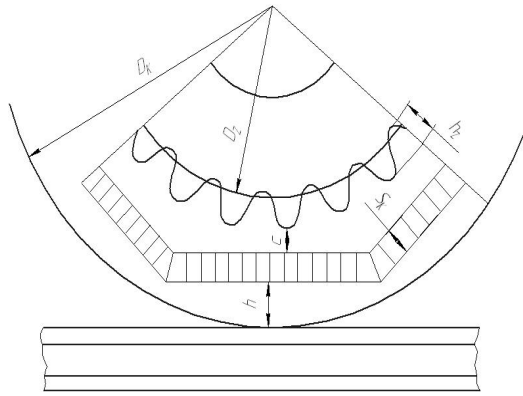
Схема вписування великого зубчастого колеса в габарит рухомого складу
